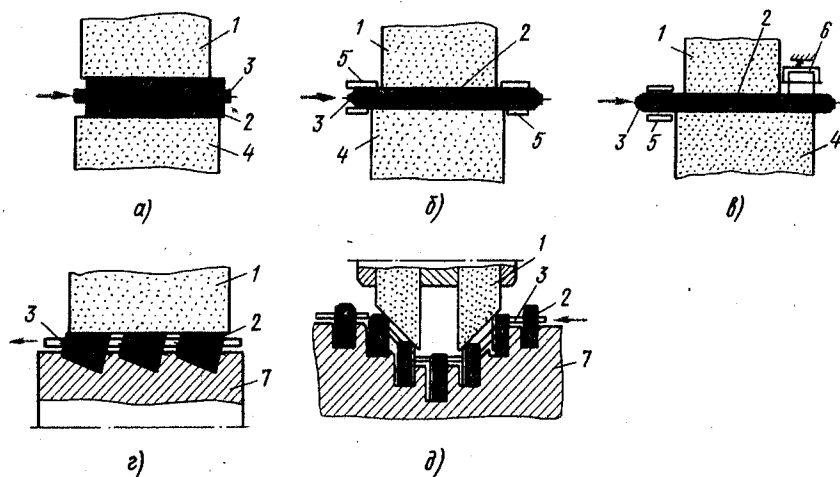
Базирование заготовок при шлифовании напроход:
